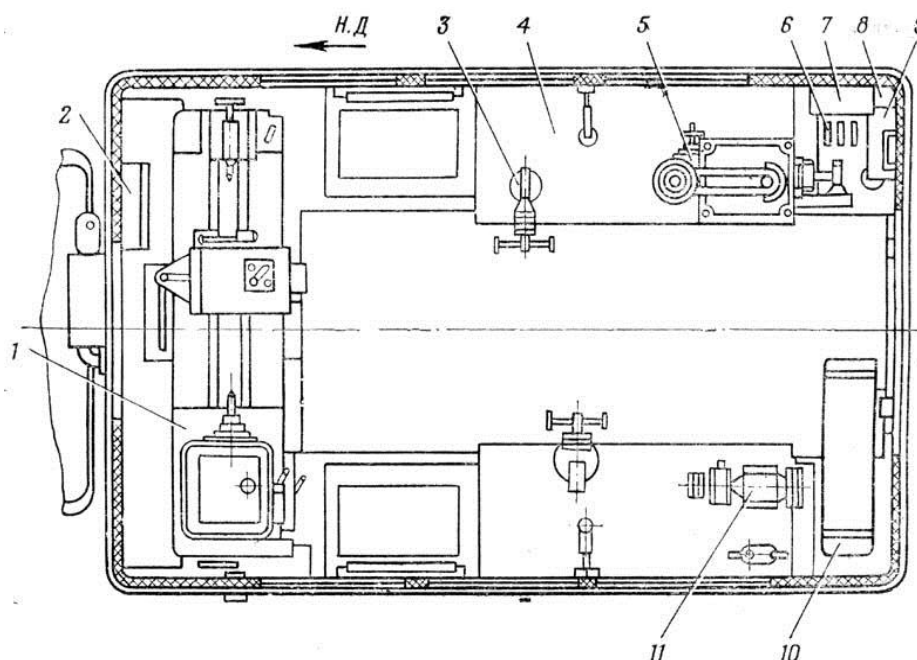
План размещения оборудования в кузове МРМ: 1 – токарно-винторезный станок; 2 – щит управления генератором; 3 – тиски; 4 – верстак; 5 – настольно-сверлильный станок; 6 – крепление оружия; 7 – щит с автоматической защитой; 8 – огнетушитель; 9 – ящик для аптечки; 10 – отопительная установка палатки; 11 – электрозаточной станок
